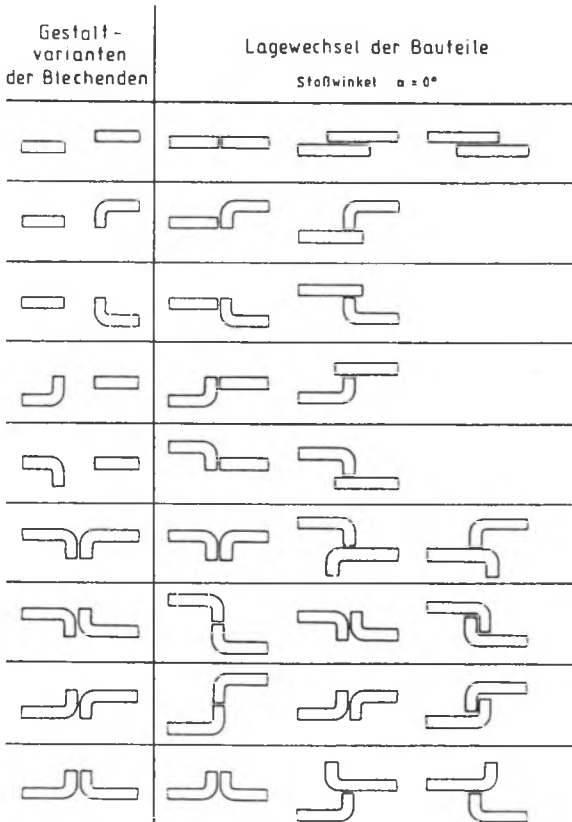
Varianten der Fugenlagen dünner Bleche, entstanden durch Lagewechsel der Schweißbauteile bzw. Lagewechsel bezüglich Teiloberflächen der Schweißbauteile. Stoßwinkel der Bleche $= 0^\circ$.
